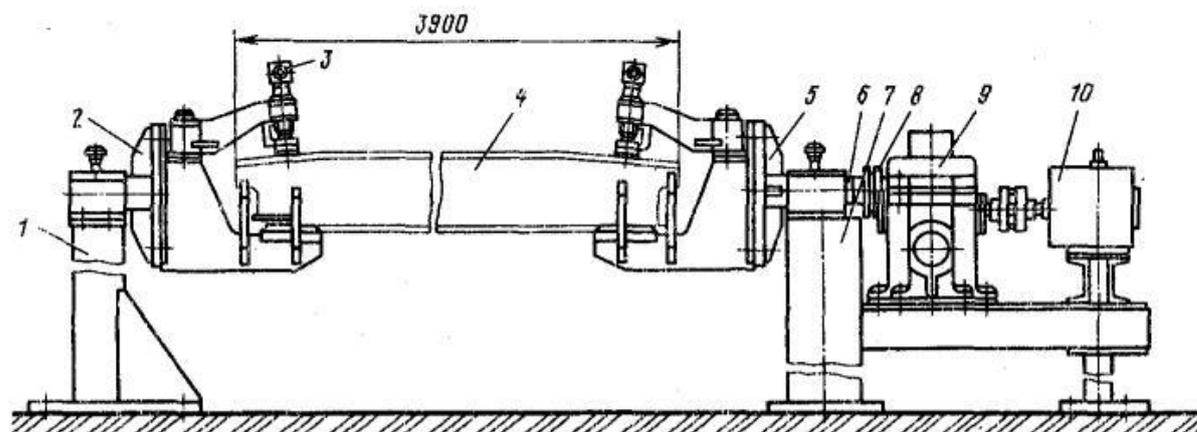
Кантователь для сборки и сварки продольной балки тележки
